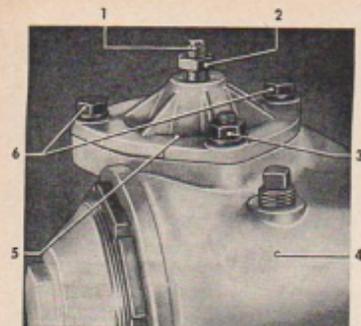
Lenkgehäusedeckel auf Lenkgehäuse aufgeschraubt
